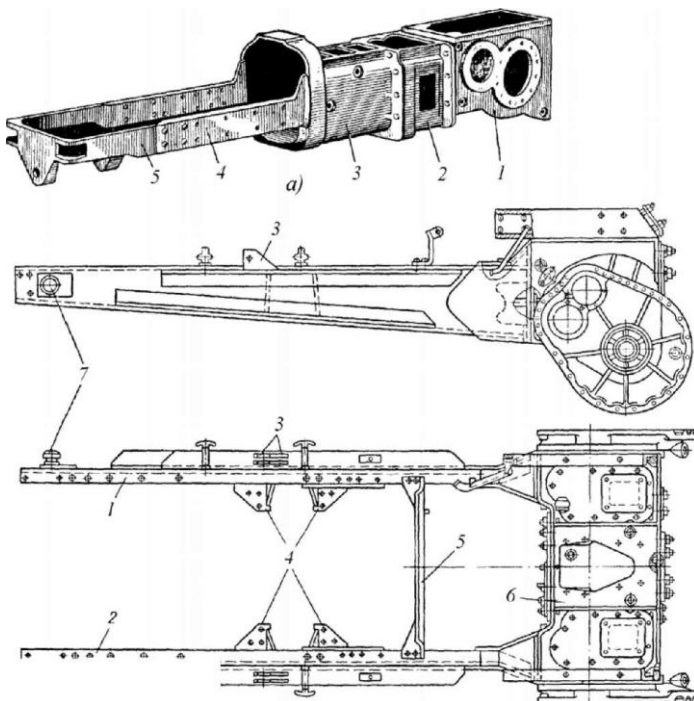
Напіврамний остов тракторів: а - МТЗ-80: 1 - корпус центральної передачі; 2 - корпус коробки передач; 3 - корпус зчеплення; 4 - лонжерони; 5 - брус; б - Т-100М: 1,2 - лонжерони; 3 - косинки; 4 - кронштейни; 5 - опора коробки; 6 – картер заднього мосту; 7 – пальці.
